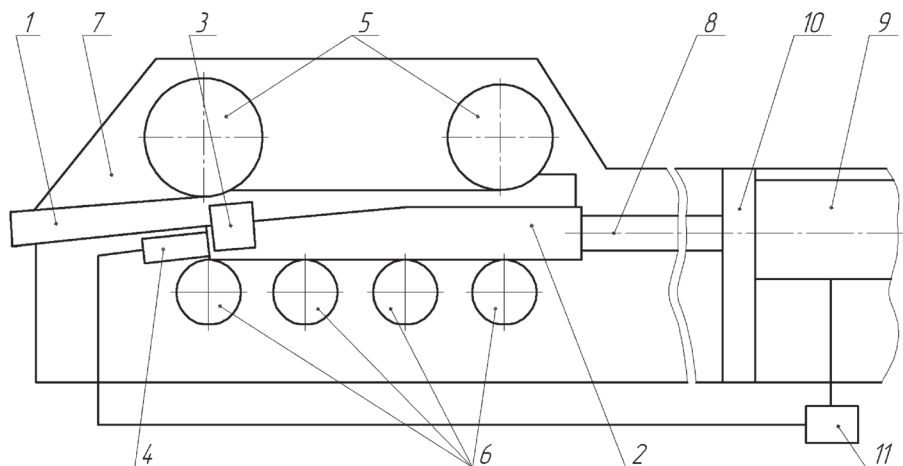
Принципиальная схема стана для прокатки заготовок направляющих элементов пневмоподвески: 1 – заготовка; 2 – оправка; 3 – зажим; 4 – гидроцилиндр зажима; 5 – валки; 6 – опорные ролики; 7 – станина клетки; 8 – шток главного гидроцилиндра; 9 – главный гидроцилиндр; 10 – станина привода; 11 – гидростанция
